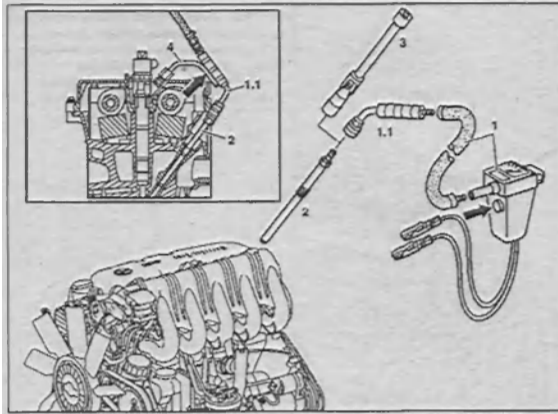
Проверка компрессии (на двигателях 612.981):
